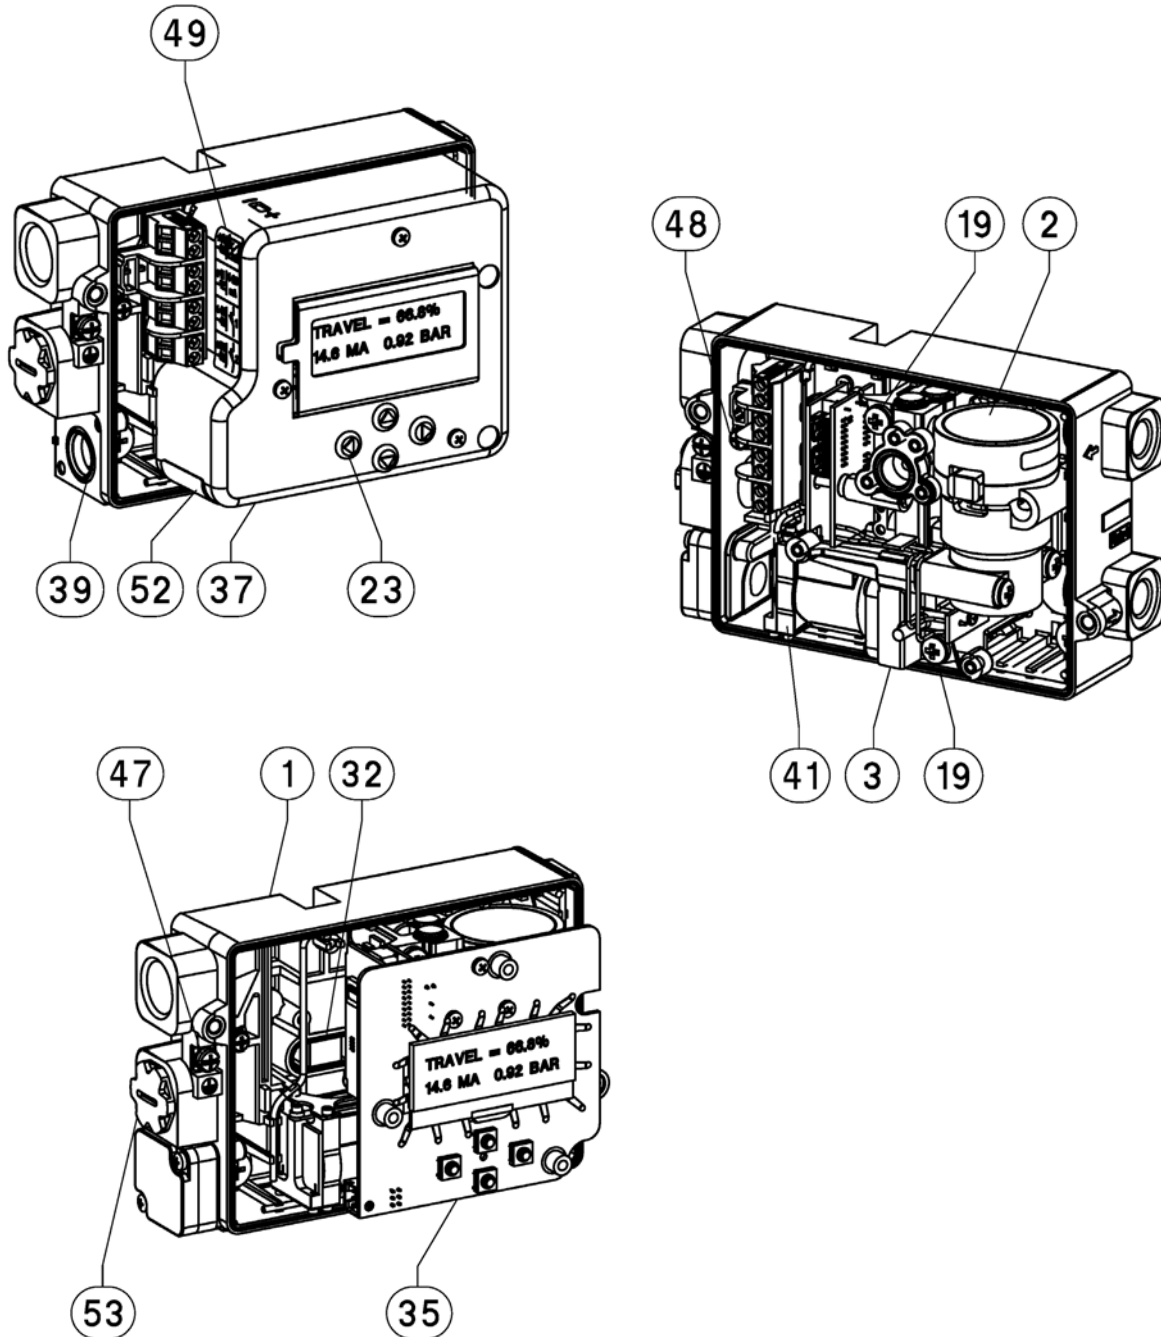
Цифровой контроллер клапана FIELDVUE DVC2000 в сборе, корпус А
